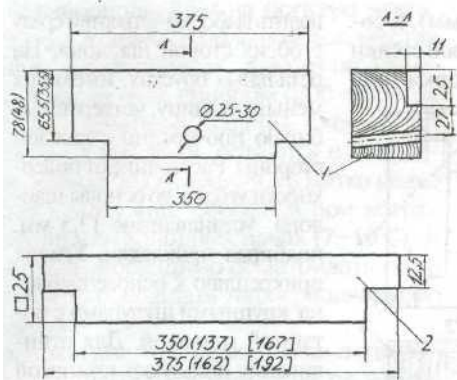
Бруска каркаса передней и задней стенок корпуса: 1 — верхний брусок передней стенки (в скобках размеры верхнего бруска задней стенки); 2 — нижний брусок (в круглых скобках размеры бокового бруска передней стенки; в квадратных — бокового бруска задней стенки)
